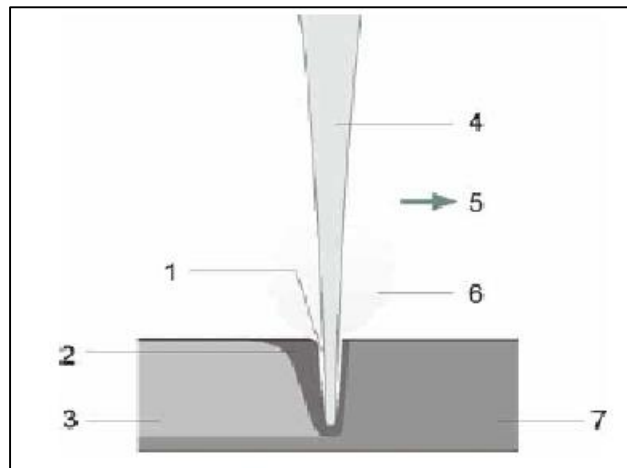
Princípio da soldadura por penetração. 1 – *keyhole*; 2 – material fundido; 3 – cordão de soldadura; 4 – raio *laser*; 5 – sentido da soldadura; 6 – vapor de metal; 7 – peça de trabalho.
